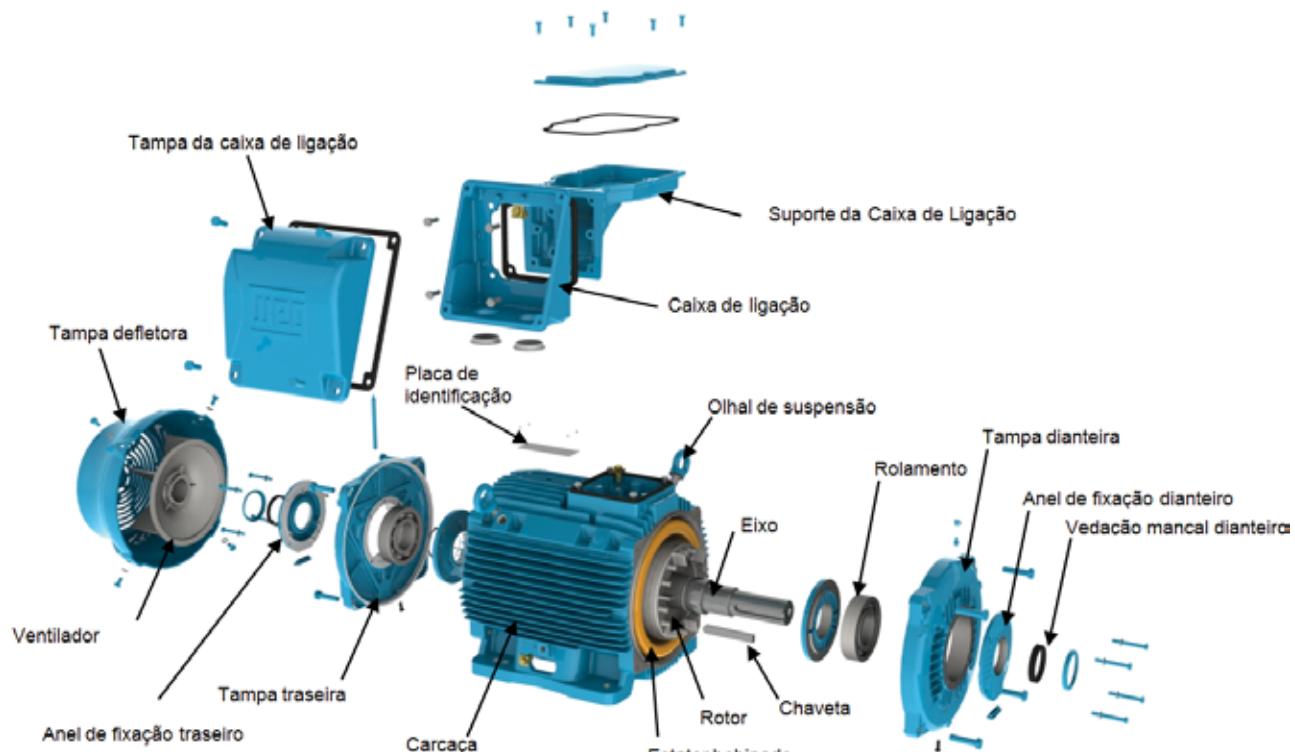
Vista explodida dos componentes de um motor W22.
